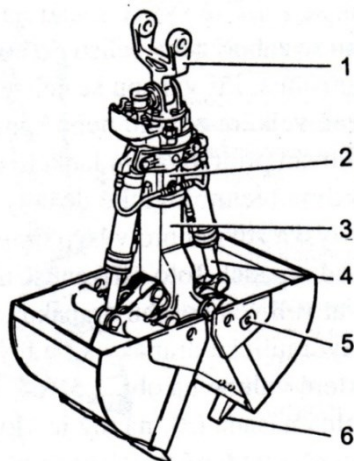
Pracovní zařízení u rypadel s hydraulickým drapakem
